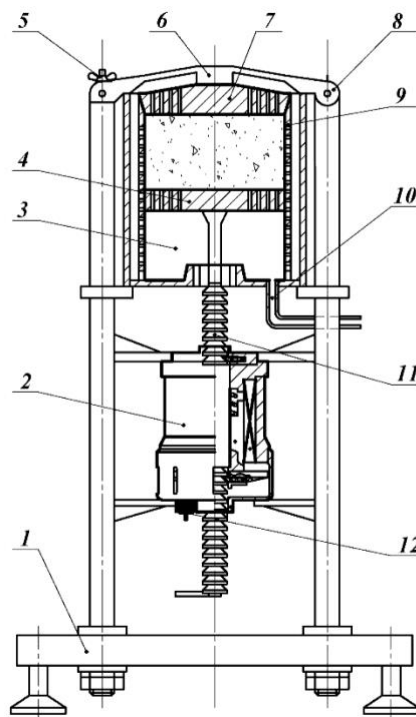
Конструкция устройства для отжима сока с шаговым ЛЭМД
